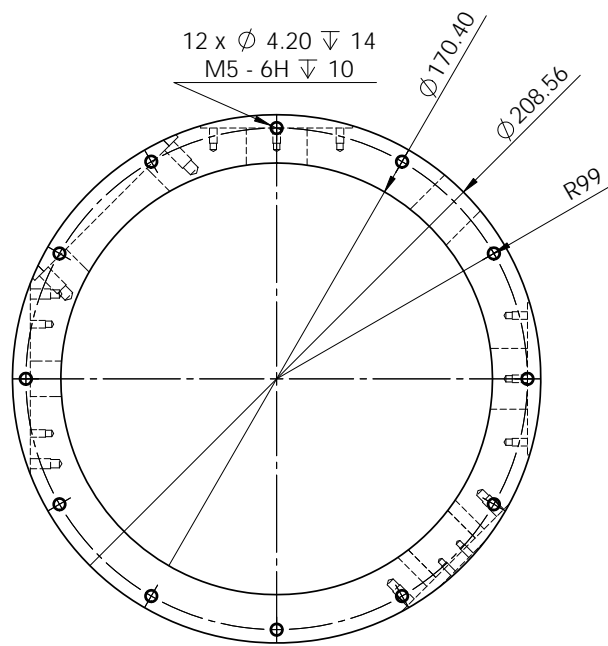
Technische Zeichnung der Vakuumröhre, Ansicht von unten.
